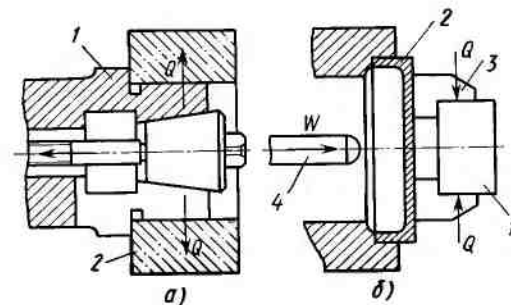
Зажимные устройства приспособлений: а — цанговый механизм; 1 — цанга, 2 — заготовка; б — мембранный патрон; 1 — заготовка, 2 — мембрана, 3 — кулачки, 4 — пружина
